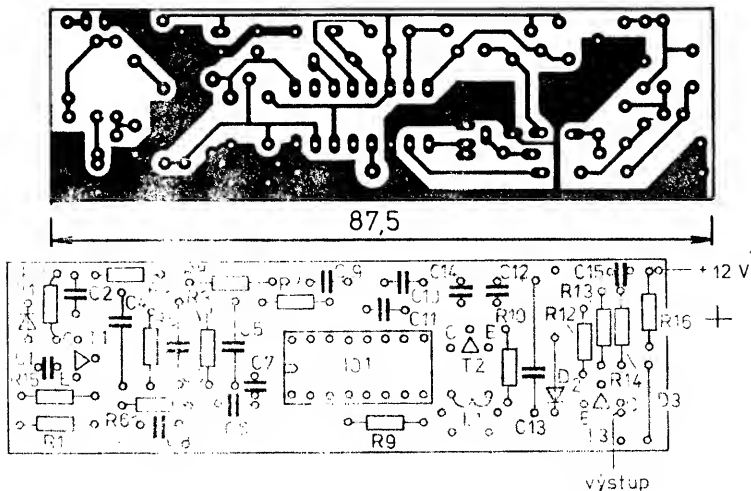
Deska s plošnými spoji W205 a rozmístění součástek obvodu z obr. 43
